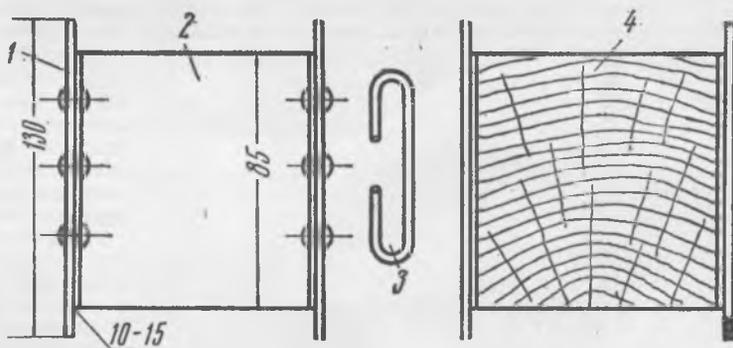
1 — наклепанные планки; 2 — стальная подсобная шинка; 3 — скобка для фиксации загнутых пластинок; 4 — шинка с распаренной пластинкой.
